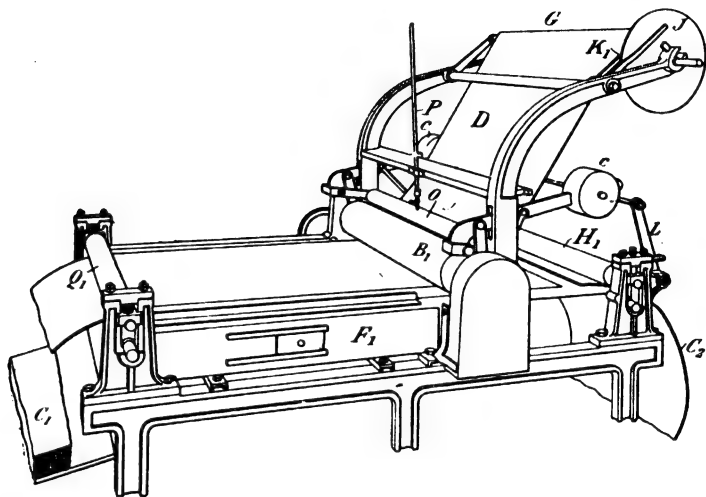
Machine à coller Siemens Brothers. Élévation.
